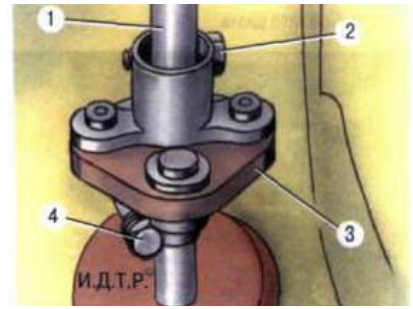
Муфта шала рулевого колеса: 1 - вал рулевого колеса; 2 - верхний стяжной болт. 3 - муфта; 4 - нижний стяжной болт
